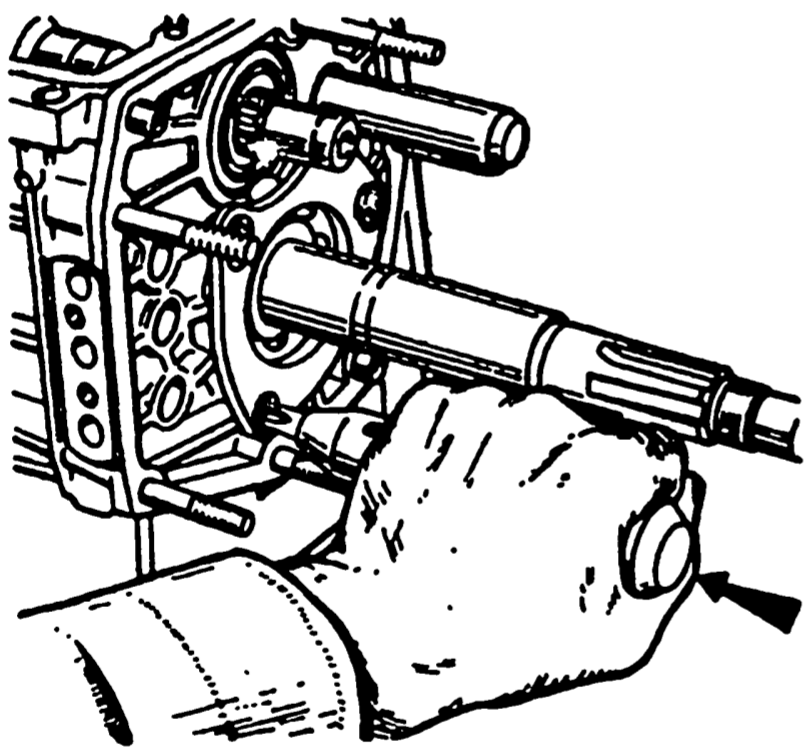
Извлечение промежуточного вала из картера коробки передач
